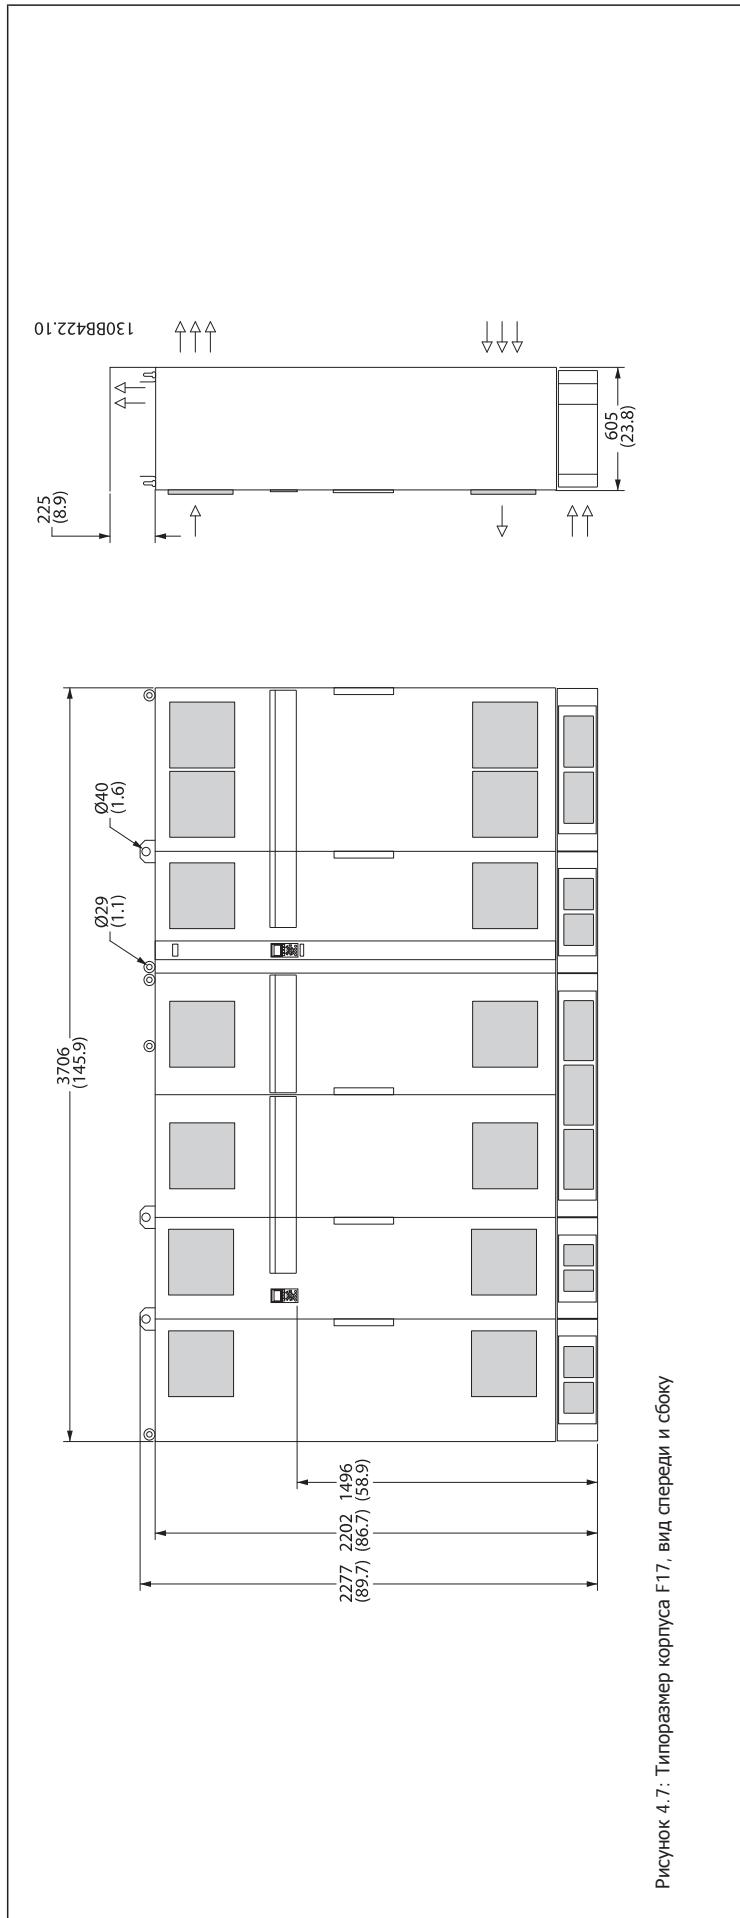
Типоразмер корпуса F17, вид спереди и сбоку
